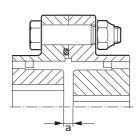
Tolerancias de montaje del acoplamiento GM
